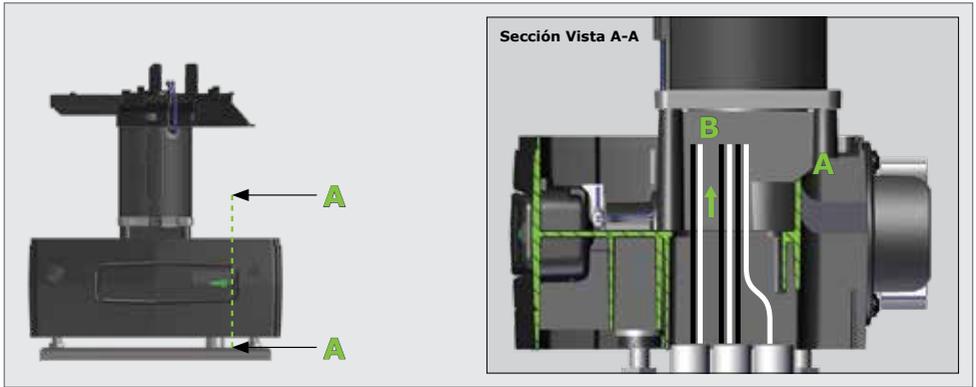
ENRUTAMIENTO DE CABLES PARA RETROAJUSTE CON CABLES MÁS CORTOS
